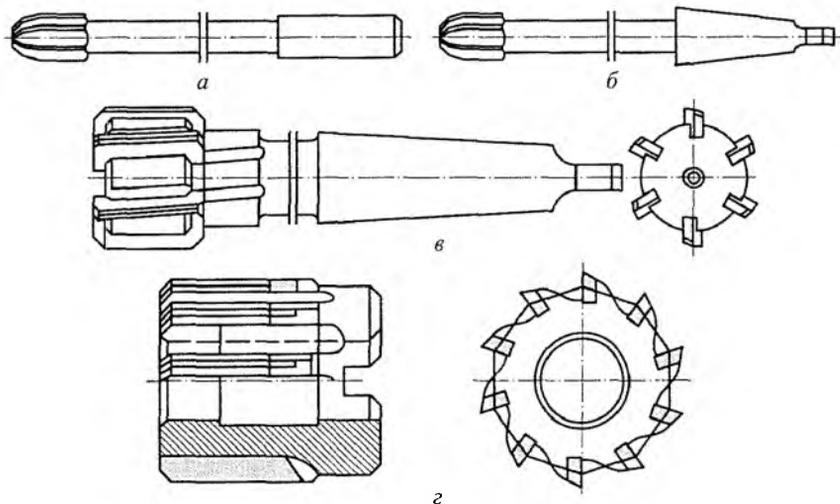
Развертки, оснащенные пластинами из твердого сплава:
